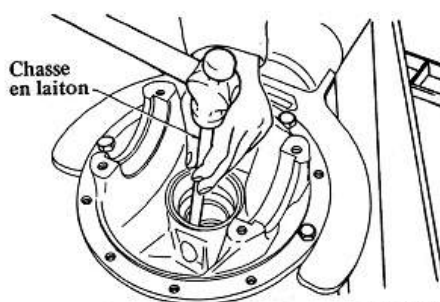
Dépose des cuvettes des roulements avant et arrière du pignon d'attaque
